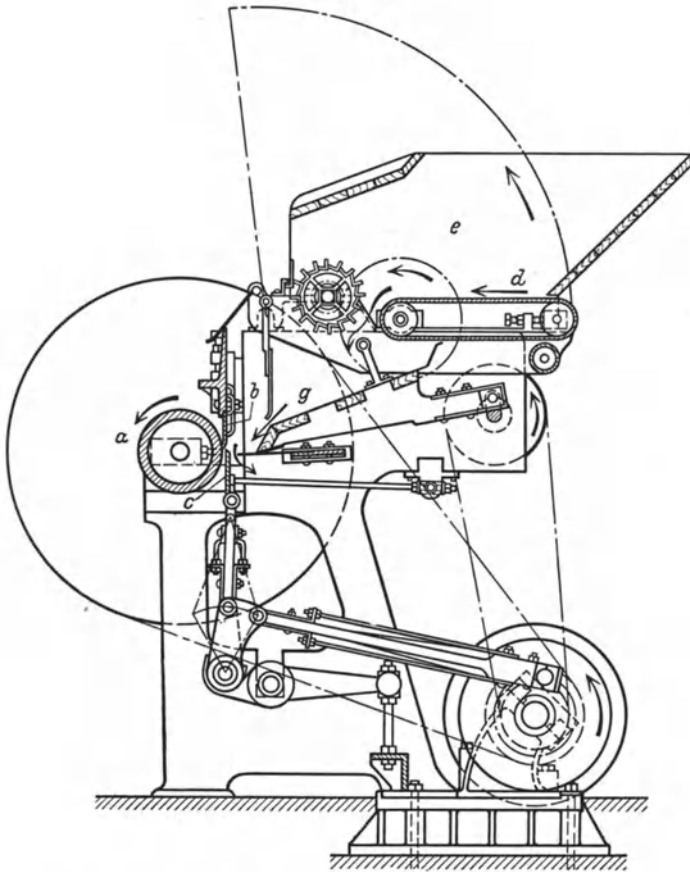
Walzen-Egreniermaschine. D.R.P. 212109.
